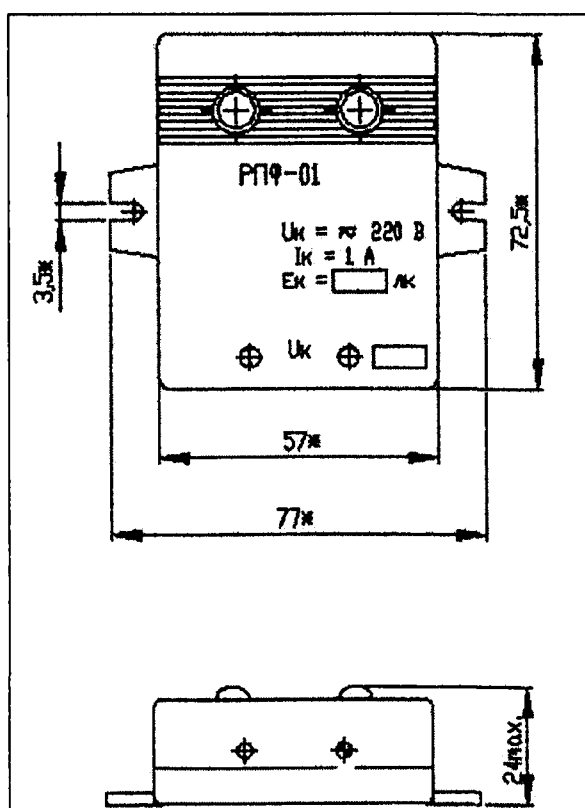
Внешний вид и габаритные размеры реле РПФ-01
